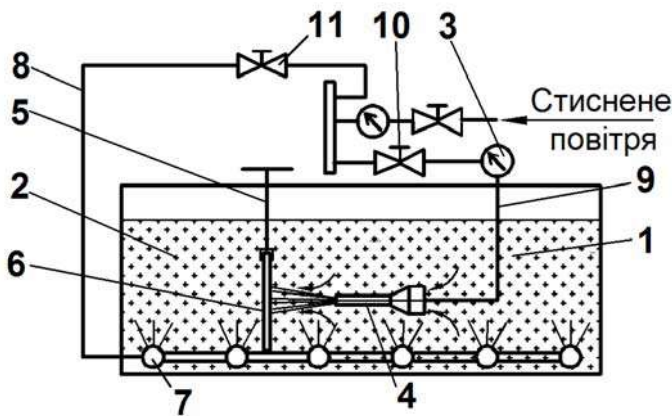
Схема струминної обробки деталей, затоплених в абразивну суспензію [130]
